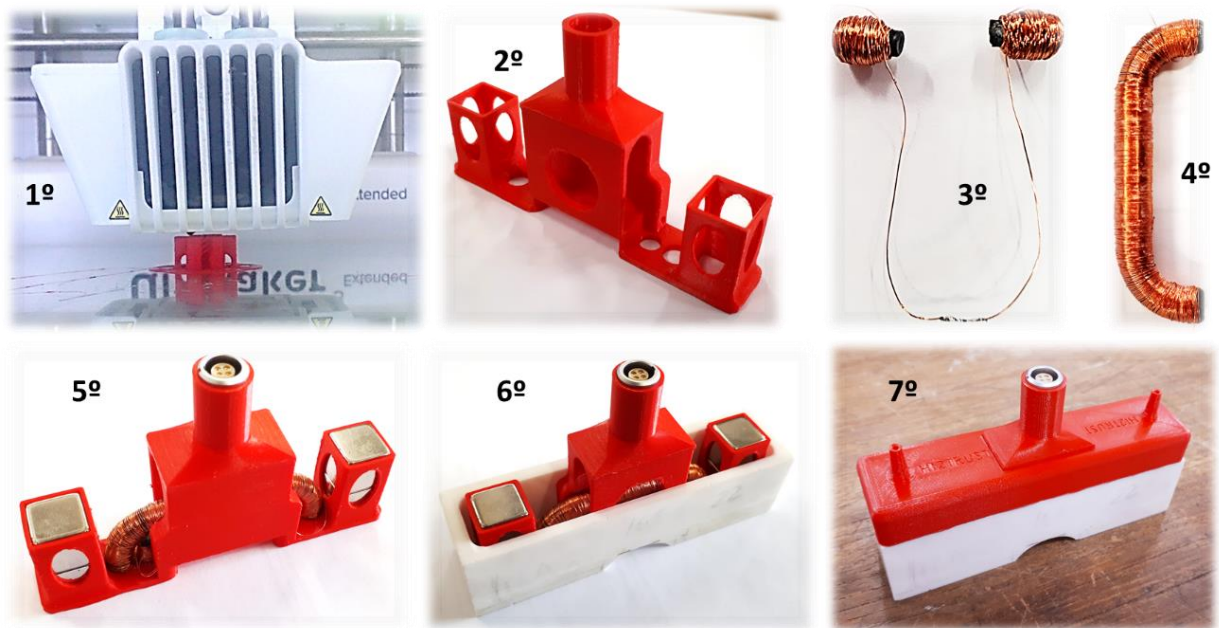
Processo de construção da sonda para inspecionar o cordão de soldadura.
